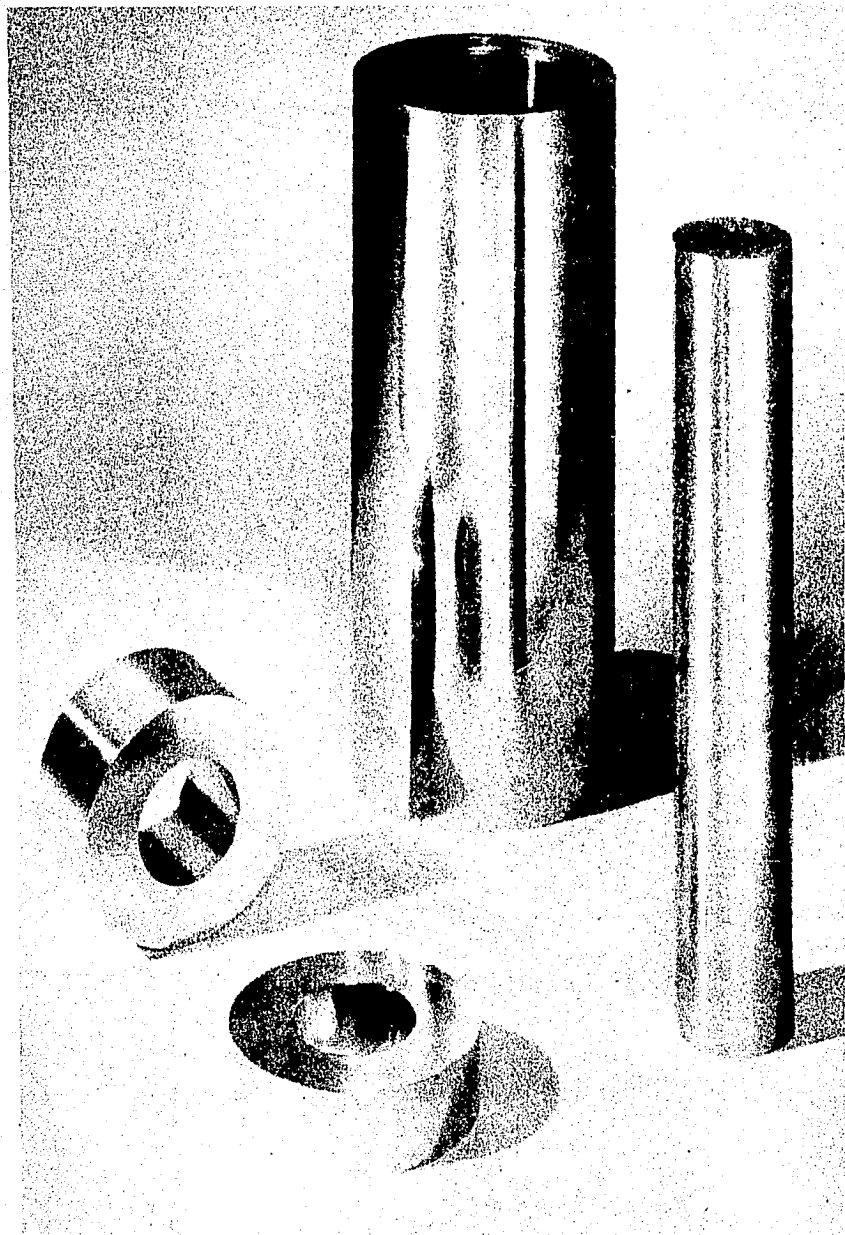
PIEZAS DE MOLDE METALICO PARA MOLDEO
